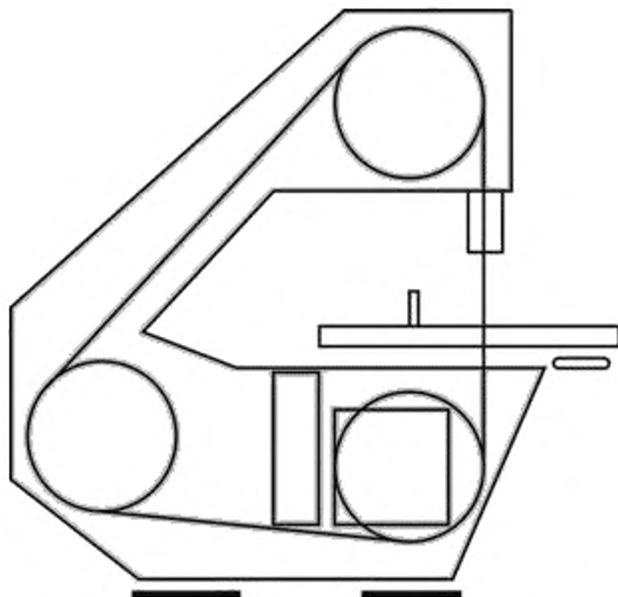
Пример ленточнопильного станка со столом, с ручной подачей и с тремя шкивами для ленточной пилы
